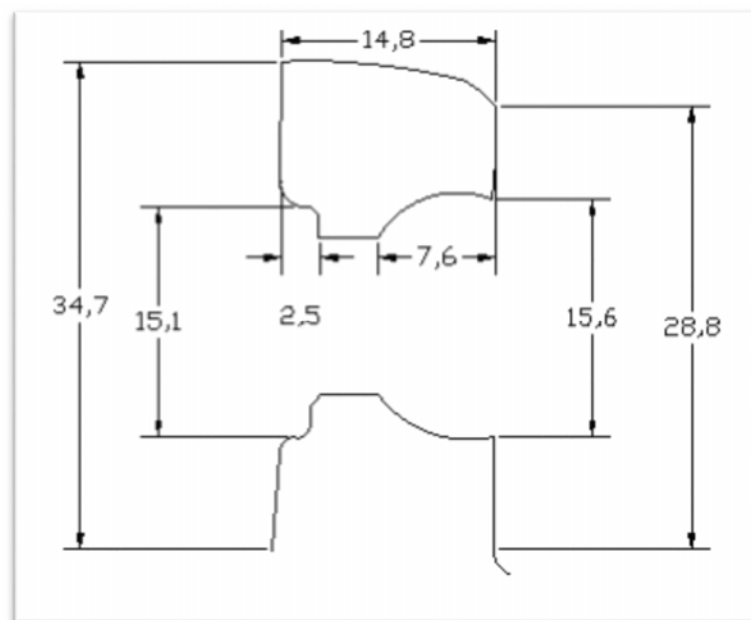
Secciones transversales de pieza soldada (Fotogrametría)
